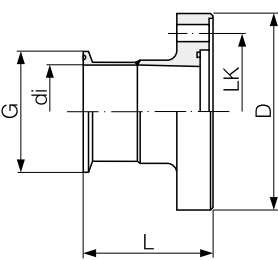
Dimensiones de la parte frontal del sensor DN 40...100
